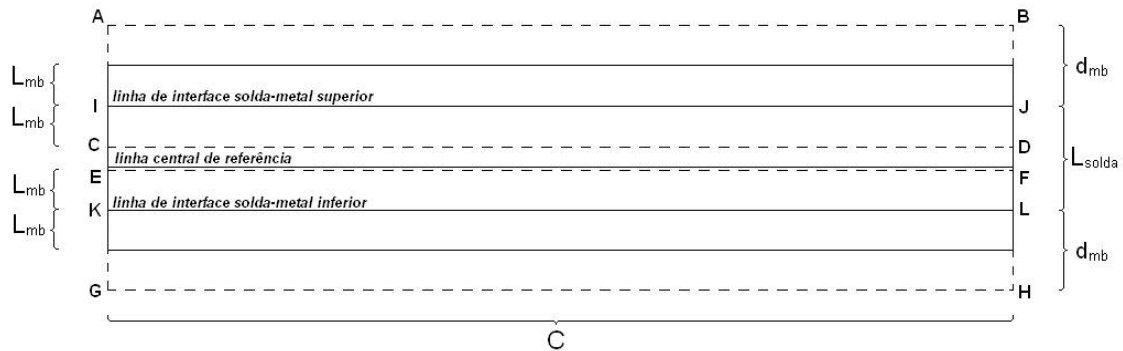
Desenho esquemático que representa as regiões de um cordão de solda a serem extraídas separadamente.
